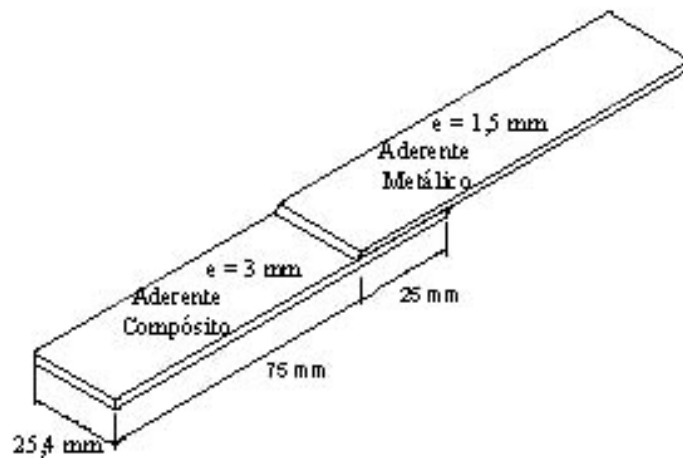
Configuração e Dimensões da Junta Simples de acordo com ASTM D5868 [40].
